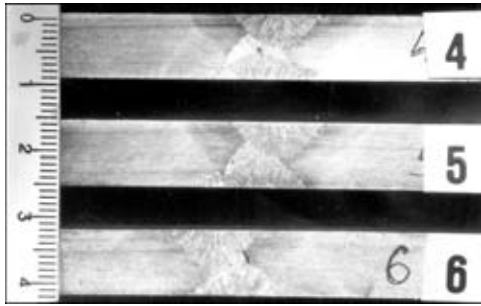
Макрошлифы сварных стыковых заводских соединений стали 16Г2АФ с несплавлениями и включениями шлака
